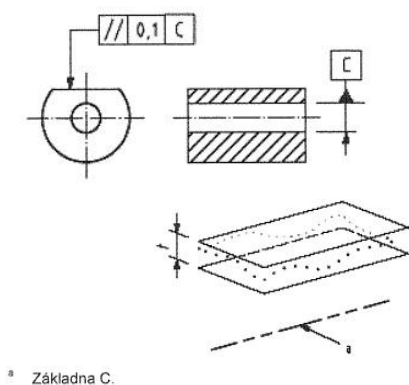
Označení a vysvětlení geom. tolerance rovnoběžnosti pro válcové tol. pole [4]
